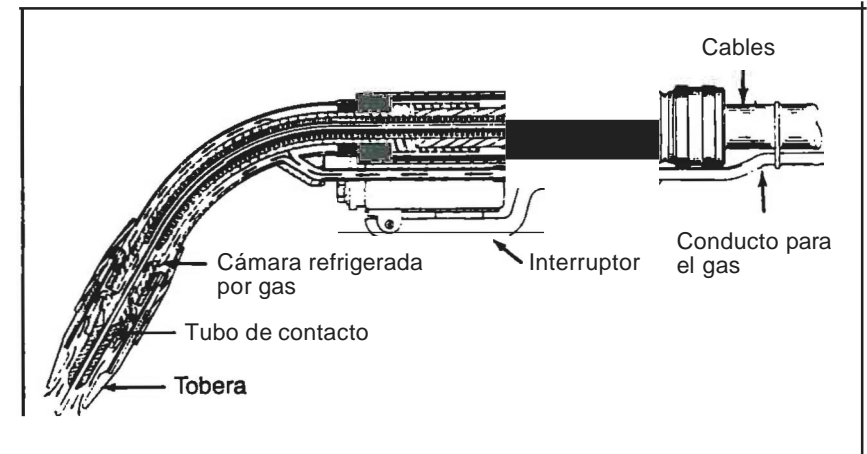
(B): PISTOLAS PARA EL SOLDEO CON PROTECCIÓN DE GAS
